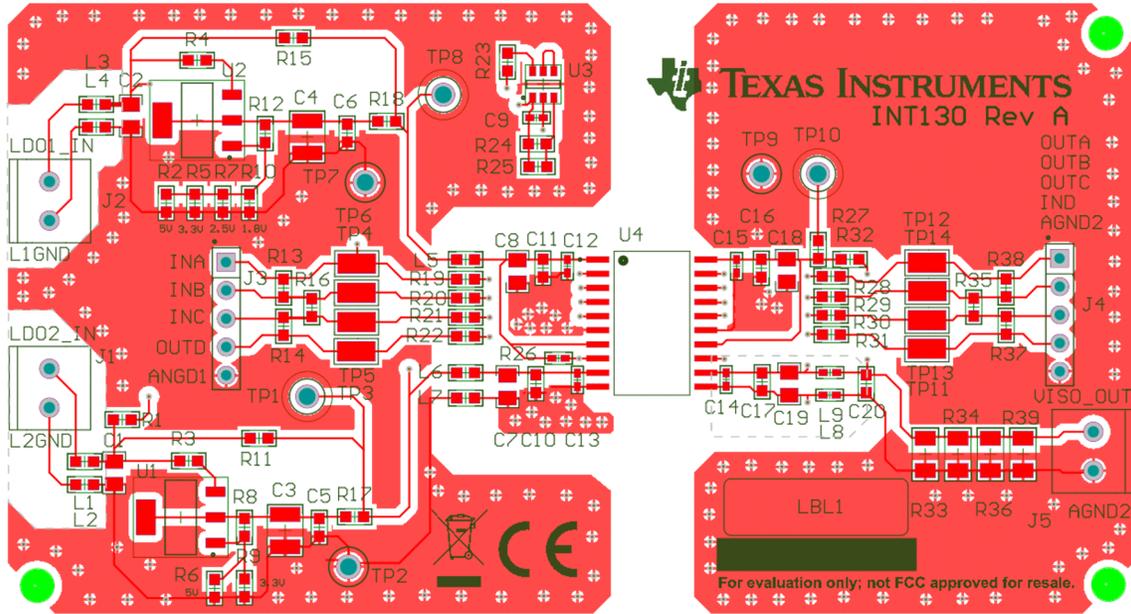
ISOW7741DFMEVM PCB 布局 - 顶层
